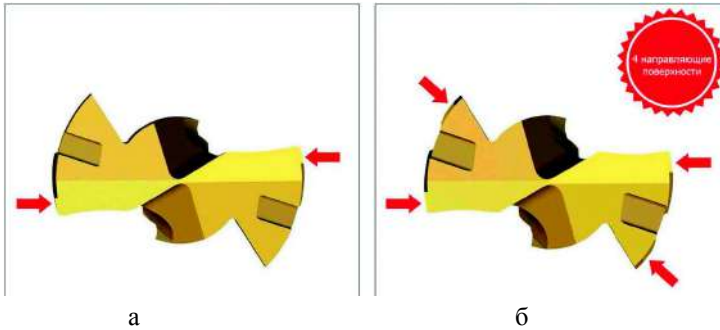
Звичайна коронка (а) та оновлена коронка із подвійною стрічкою (б)
